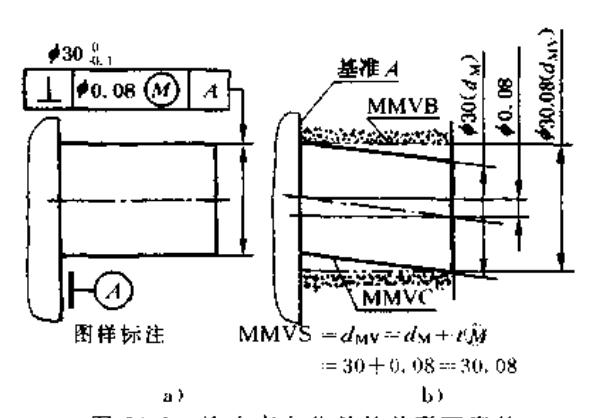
给出定位公差的关联要素的定位体内作用尺寸
